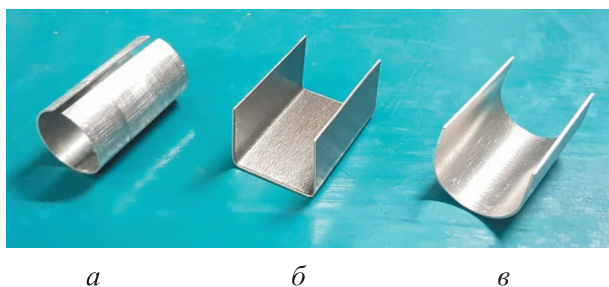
Внешний вид опытных образцов труб и профилей, изготовленных из листовых заготовок свертыванием в ЭСС:
